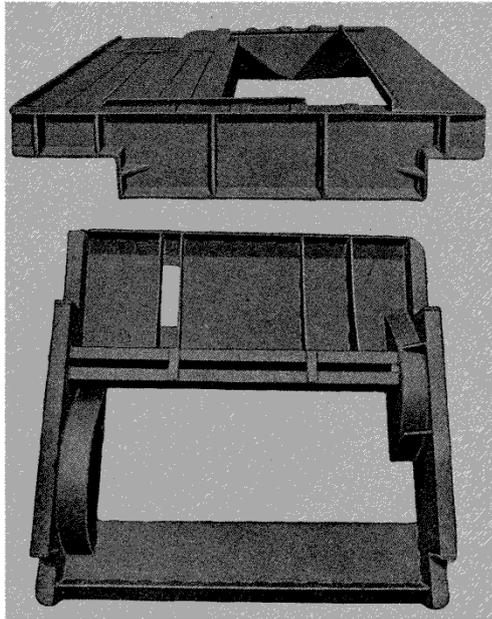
Chariot de pont roulant construit par soudure.
